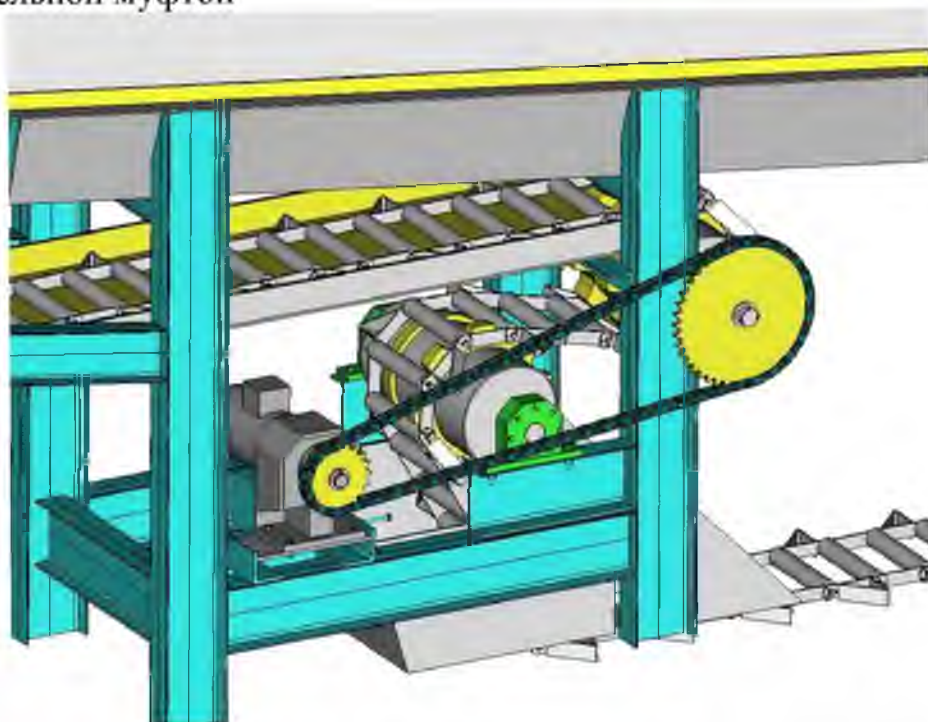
Кинематическая схема привода транспортера цепного типа ТСЦ
